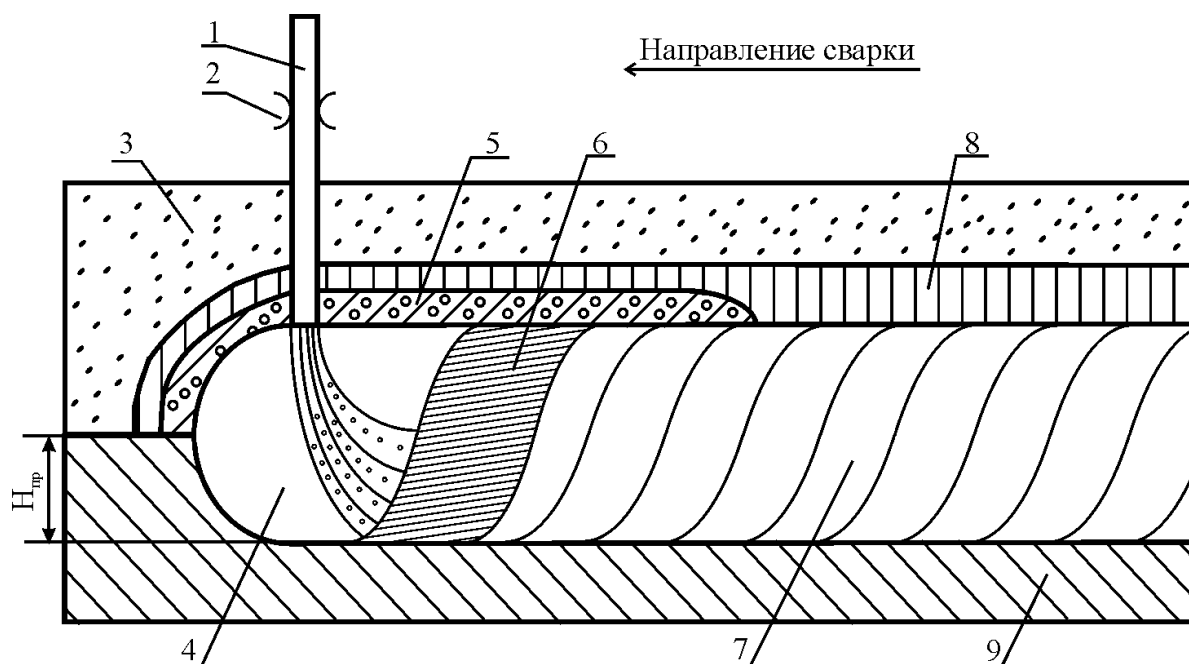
Сварка под флюсом: 1 – электродная проволока; 2 – подающий механизм; 3 – флюс; 4 – газовый пузырь; 5 – расплавленный флюс; 6 – жидкая ванна металла; 7 – сварной шов; 8 – расплавленный шлак; 9 – изделие
